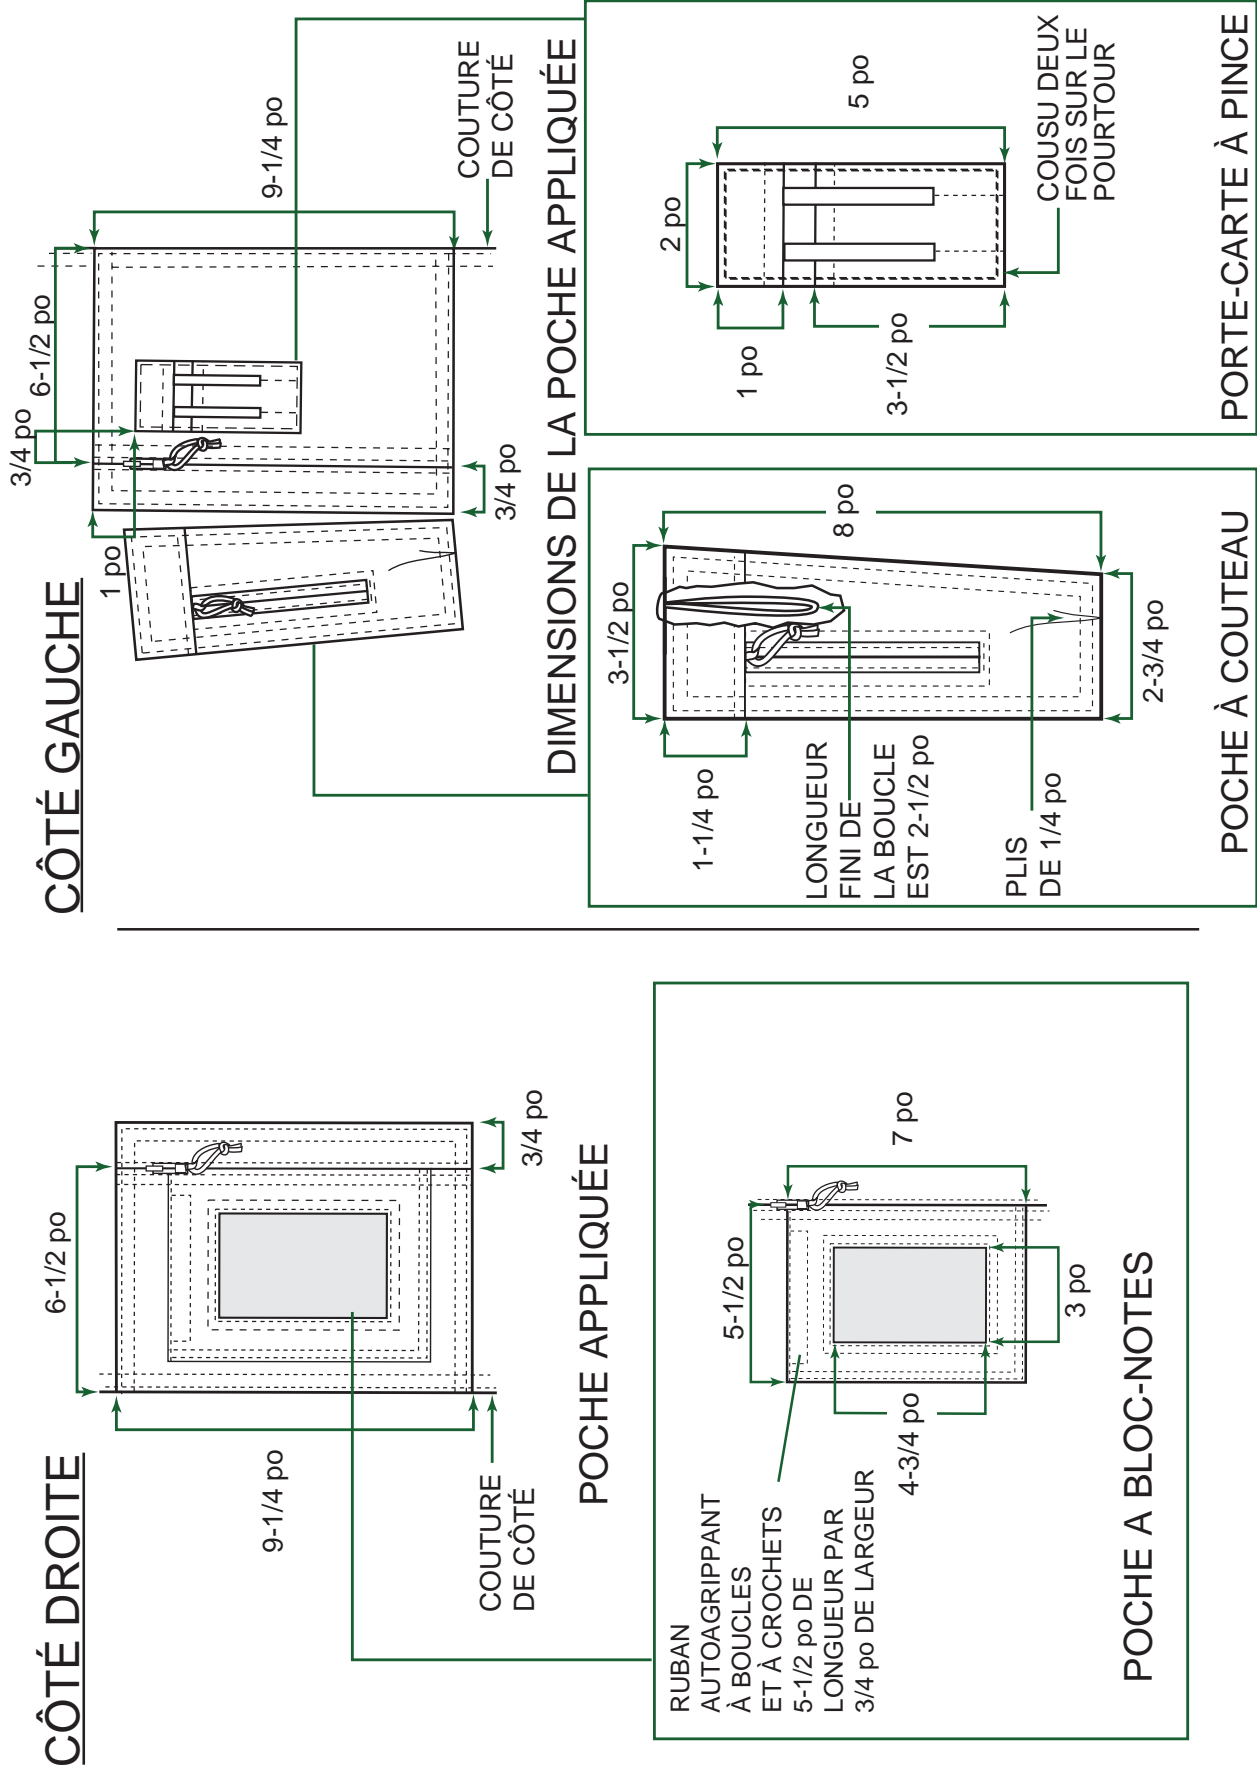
DIMENSIONS POUR LES COMPOSANTS DU BAS DU JAMBE
